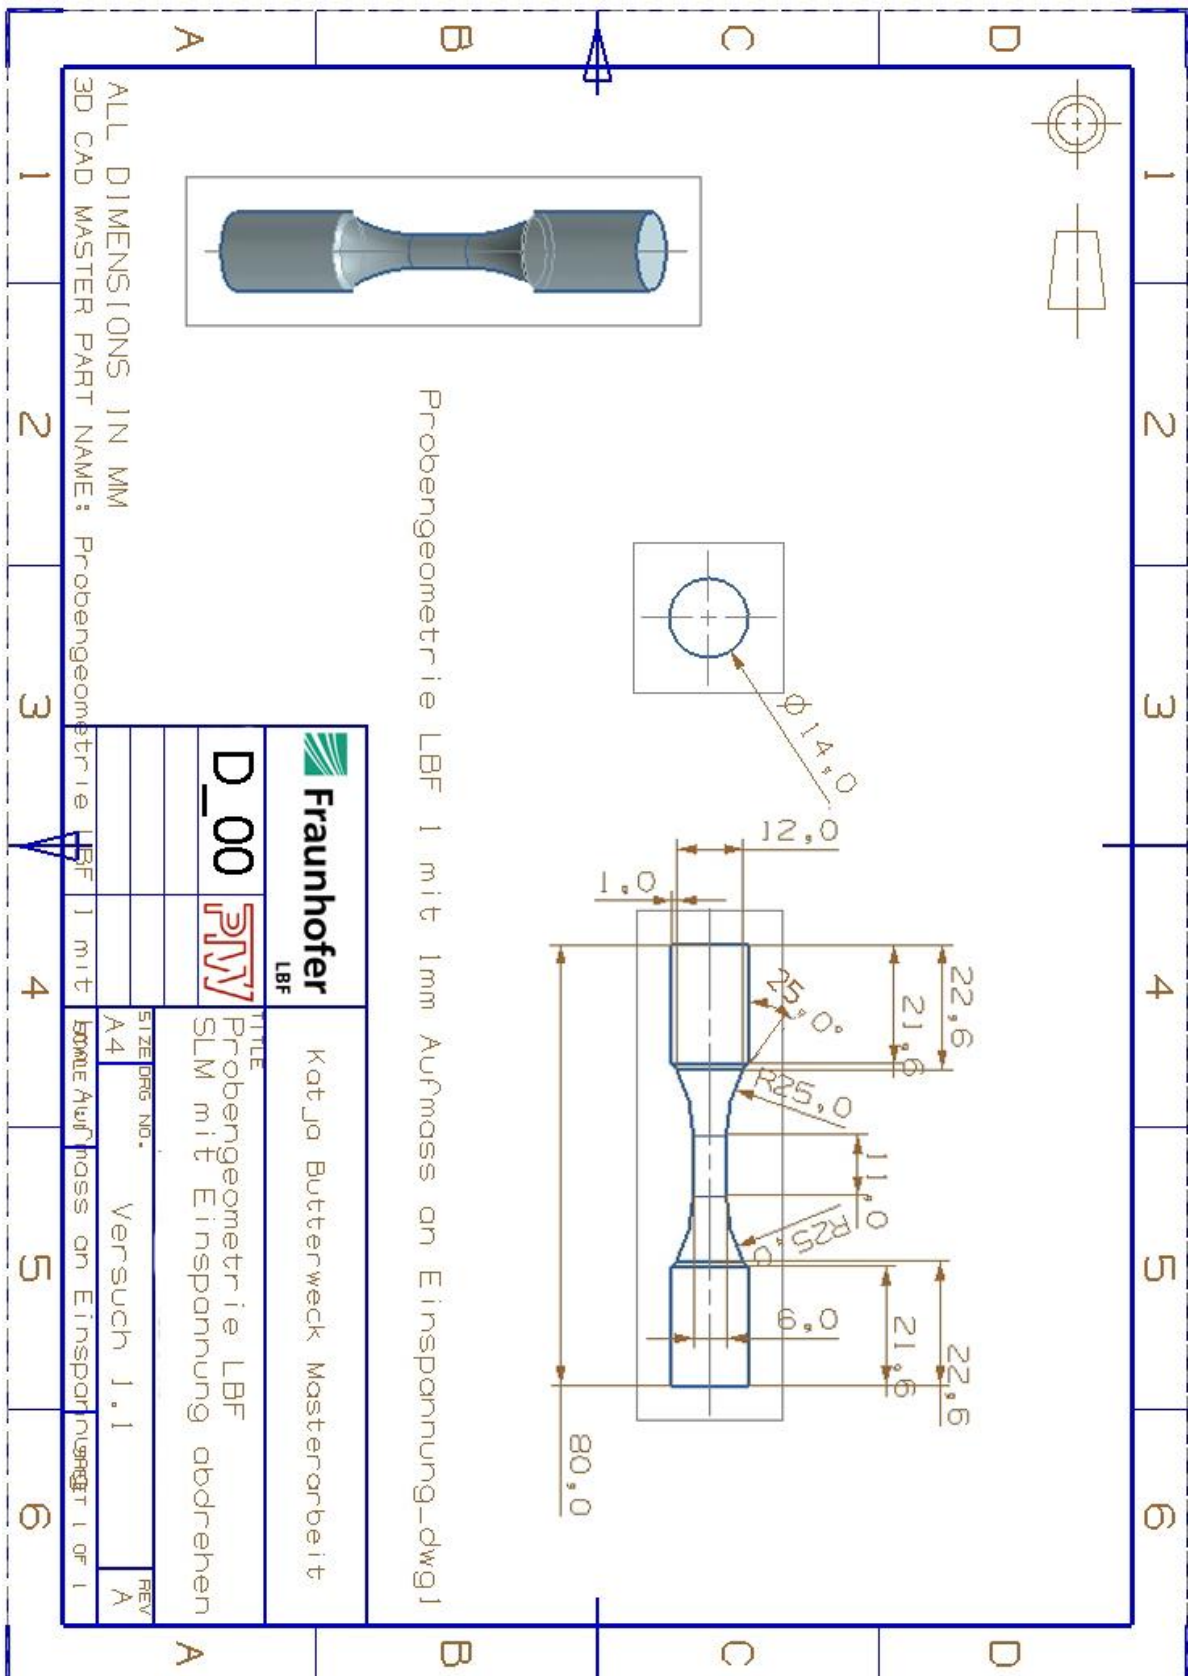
Technische Zeichnung Probengeometrie D_00
